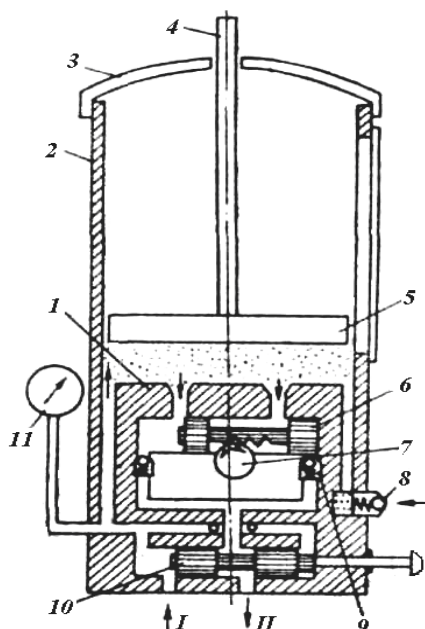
Схема ручной станции густой смазки типа СРГ
